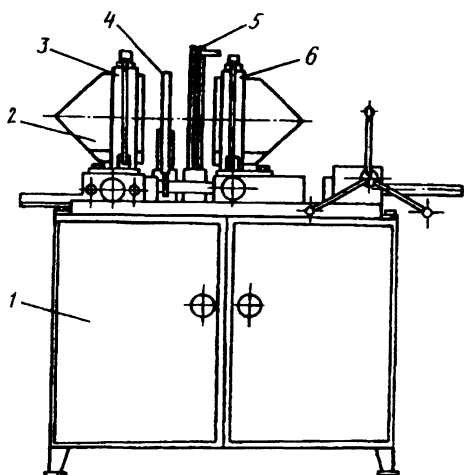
Устройство УСДП-225 для сварки соединительных деталей пластмассовых трубопроводов:
